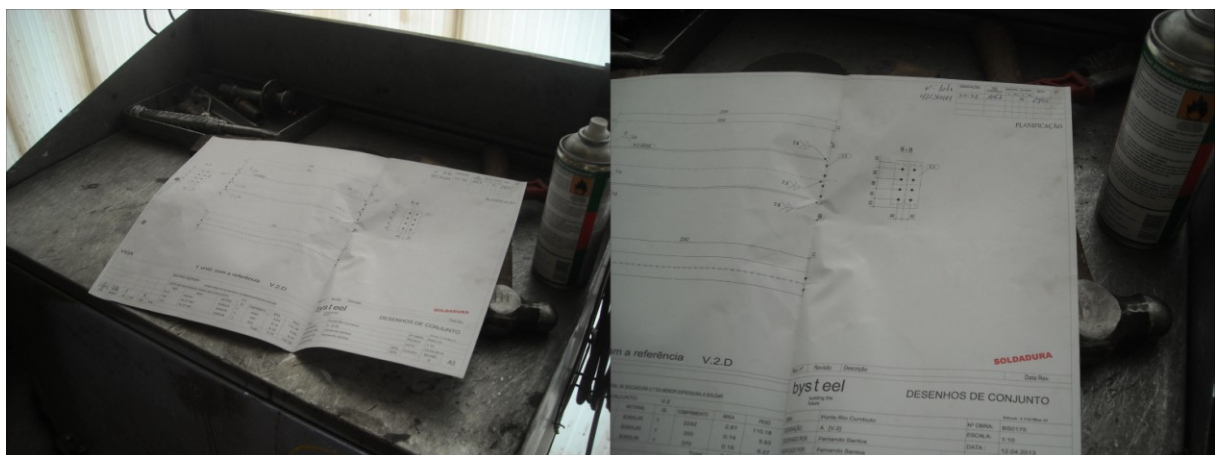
Desenhos de fabrico da Soldadura
